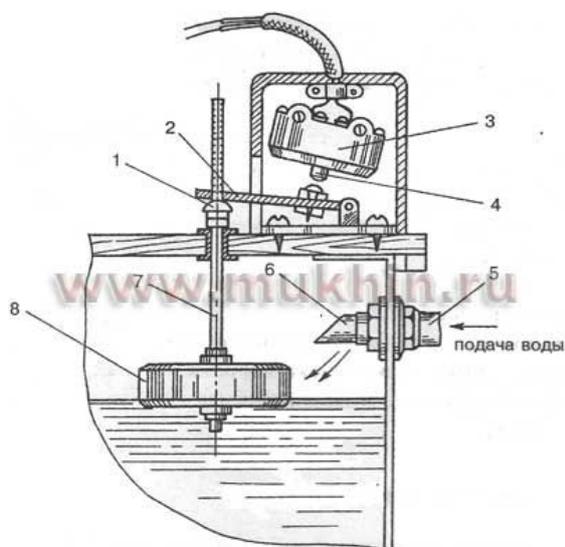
Поплавковый регулятор уровня: 1 — упор-гайка; 2 — рычаг; 3 — микропереключатель; 4 — толкатель; 5 — патрубок; 6 — отражатель; 7 — шток; 8 — поплавок
